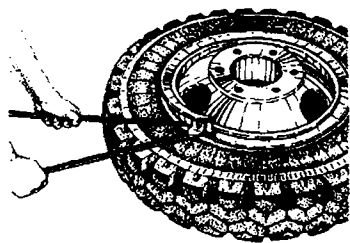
Извлечение бортового кольца из замочной канавки обода
